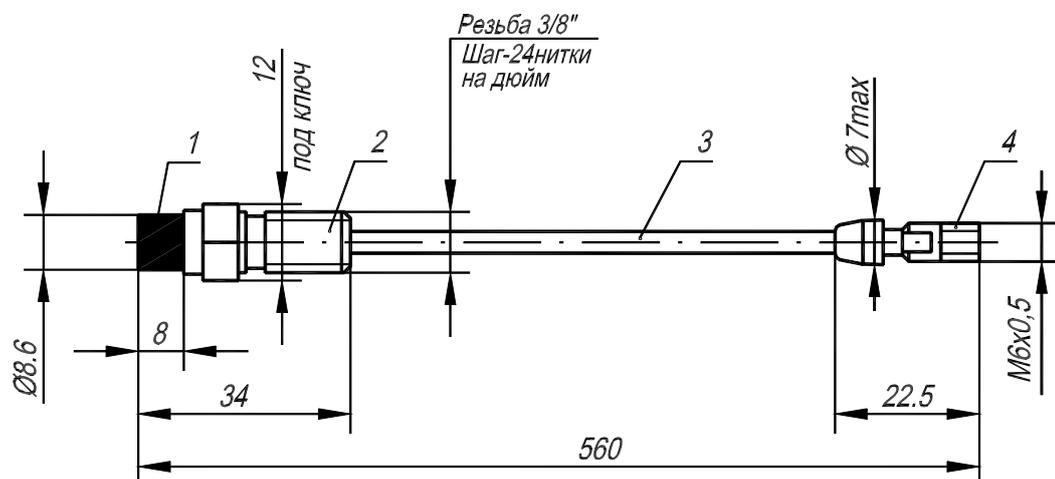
Преобразователь вихрековый ИЦФР.408113.005 (код ПВ2)
